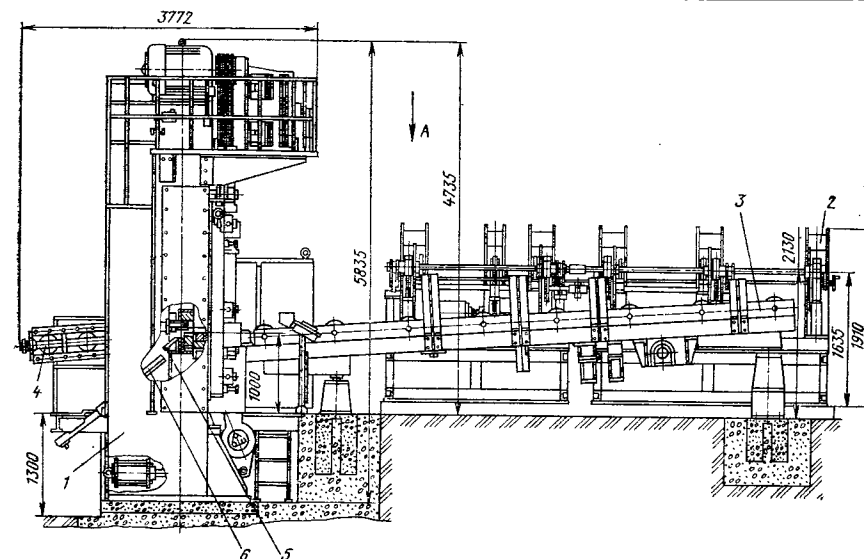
Комплекс оборудования на базе сортовых кривошипных ножниц для отрезки заготовок из круглого и квадратного проката
